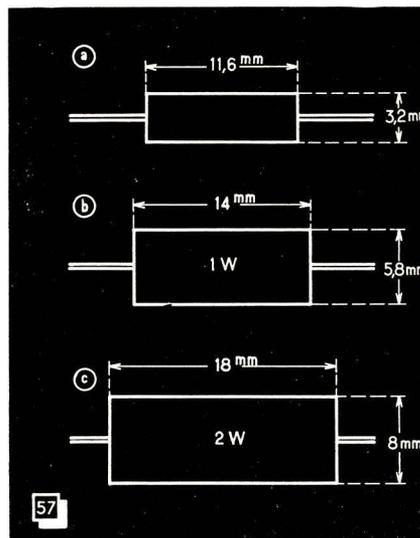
Dimensions de quelques supports pour bobines de correction.
